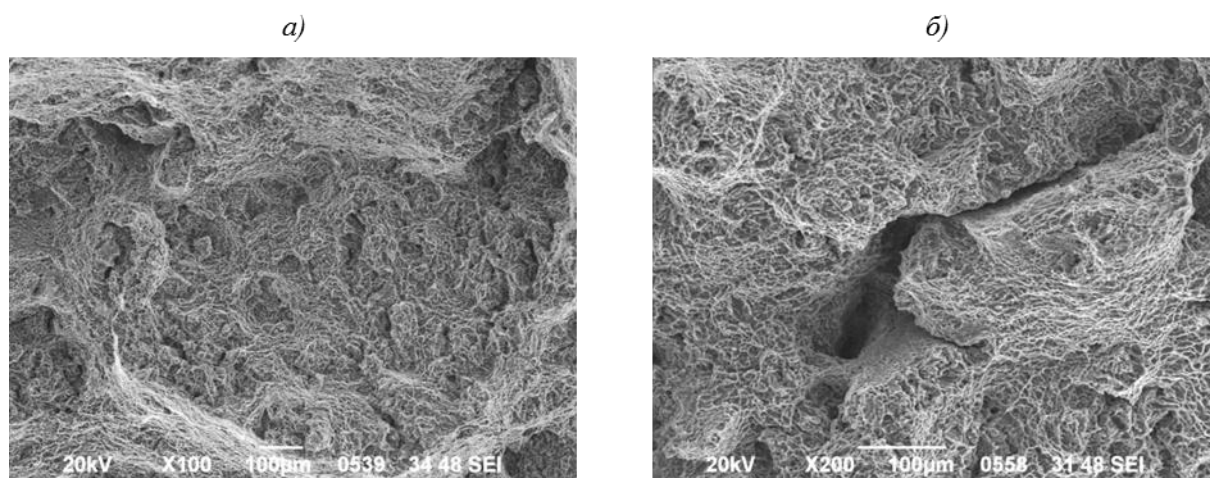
Вторичные трещины в изломе образца из сплава В-1461
